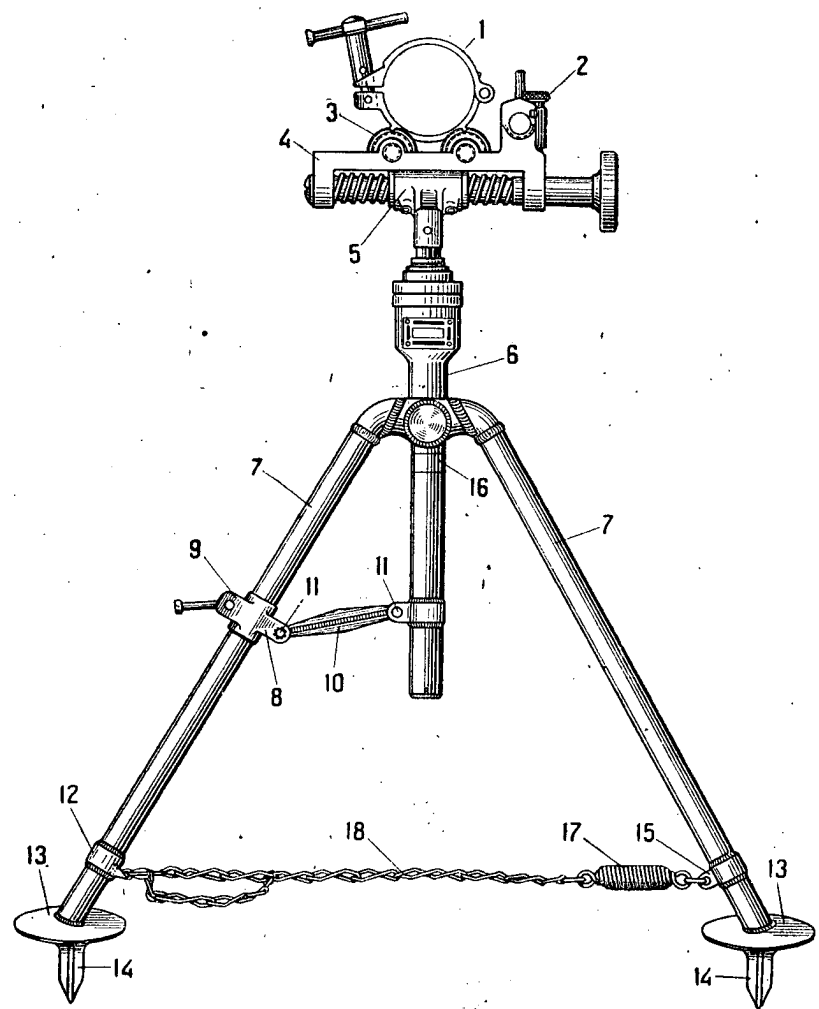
Двунога-лафет 82-мм миномета обр. 1937 г.: 1 — обойма; 2 — качающийся кронштейн прицела; 3 — амортизатор; 4 — вертикальный поворот; 5 — поворотный механизм; 6 — подъемный механизм; 7 — трубы ног; 8 — механизм грубого горизонтирования; 9 — зажимная втулка; 10 — стяжка; 11 — оси; 12 — кольцо с крючком; 13 — тарелки; 14 — сошники; 15 — кольцо с пружинной; 16 — коробка подъемного механизма; 17 — пружина; 18 — цепь
